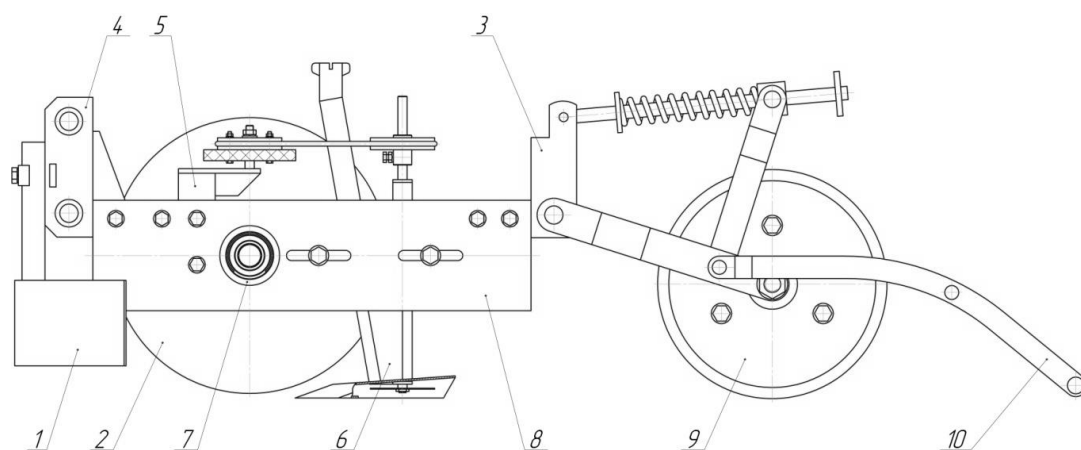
Широкополосный сошник с активным дисковым рассеивателем
